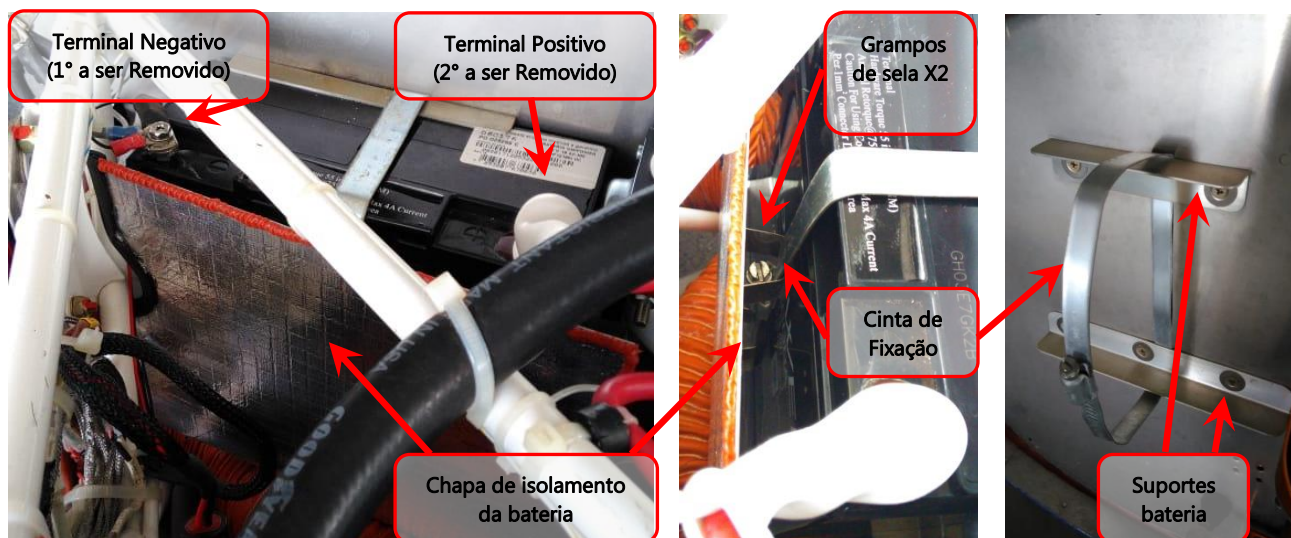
Local da Bateria, chapa isolamento e cinta de fixação
